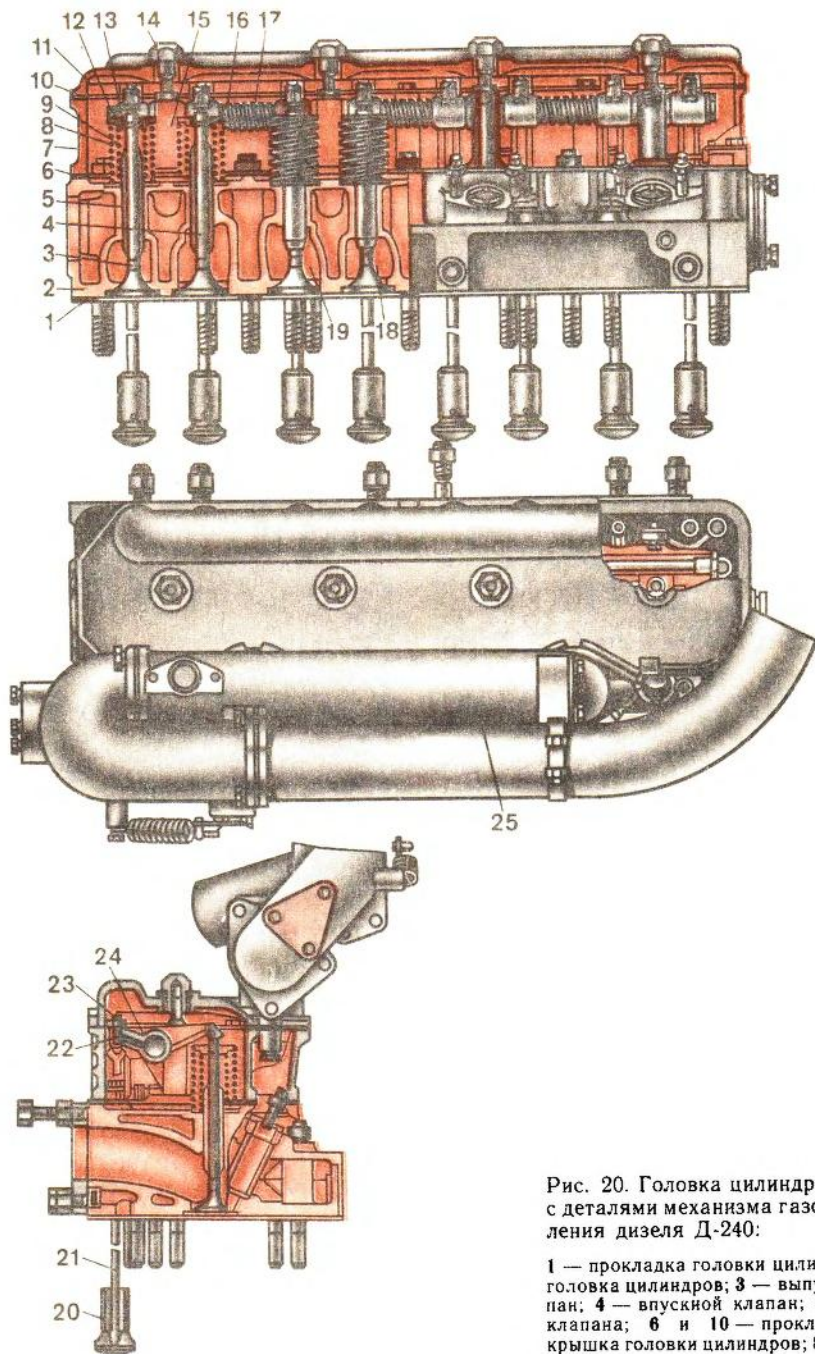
Головка цилиндров в сборе с деталями механизма газораспределения дизеля Д-240:
